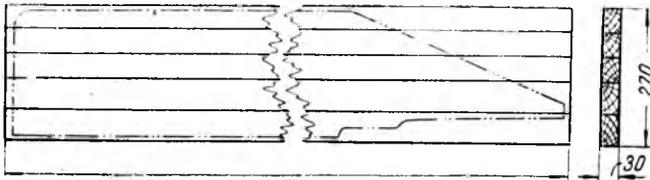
Клееная заготовка для доски наружного делителя жатки ЛМ-5
